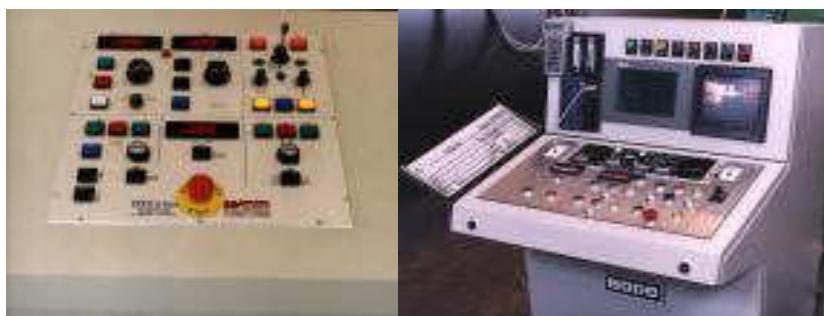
Блок управления сварочной колонной
